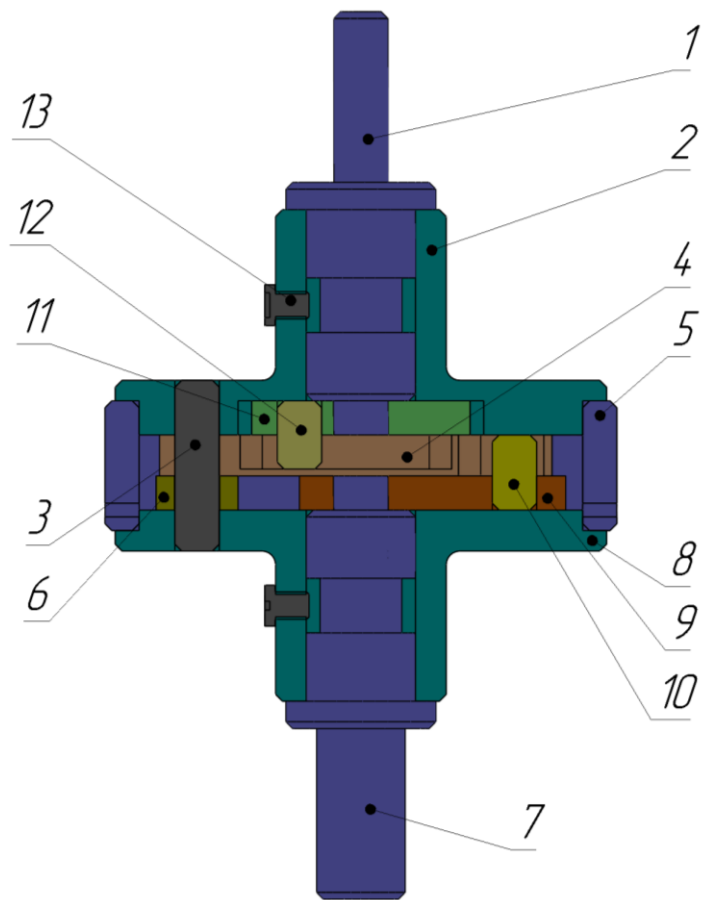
Сборка кривошипно-кулисного механизма – разрез 2
